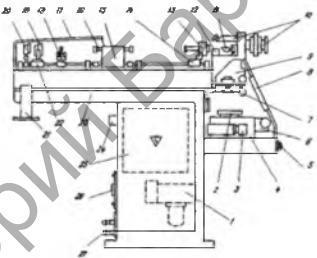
Общий вид станка мод. 4P222Ф2
